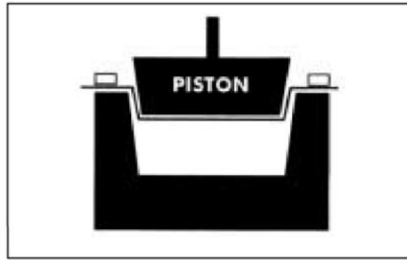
Formado a presión con ayuda de pistón, molde hembra
